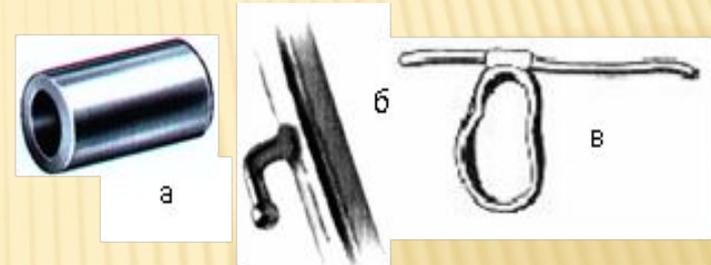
Вспомогательные элементы: а - втулка, б - крючок, в - касательная балка
